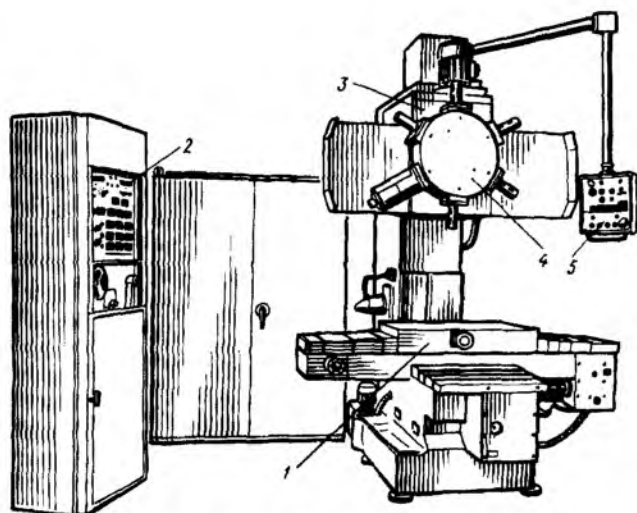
Общий вид сверлильного станка мод. 2P135Φ2
